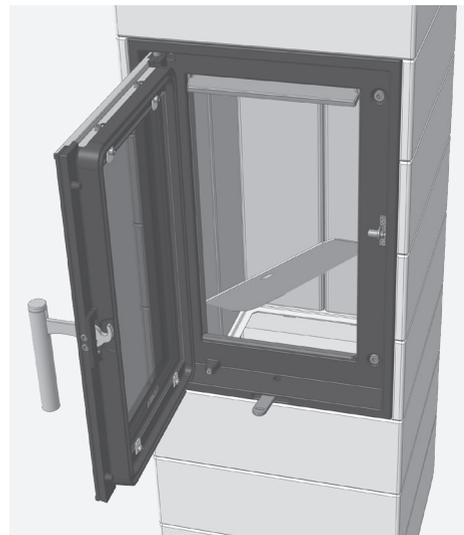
Dépose de la plaque de fond de la chambre de combustion
